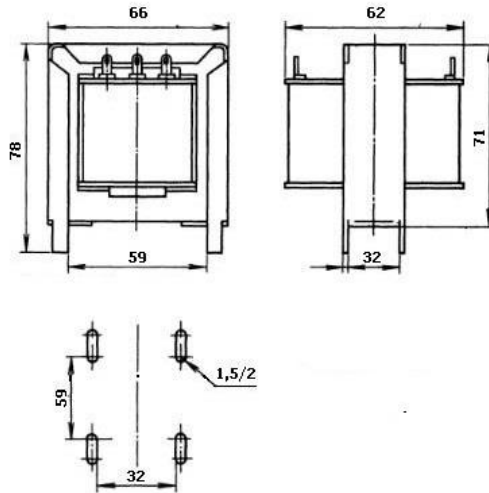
Габаритні розміри трансформатора В78386-Р1116-А "
